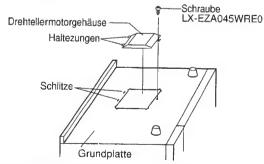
(b). Wiedereinbau des Drehtellermotorgehäuses
